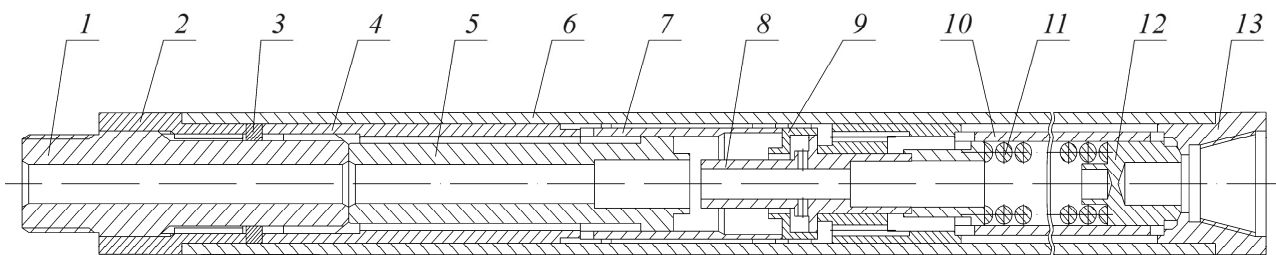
Конструкция погружного гидроударника со встроенным аккумулятором: 1 — наковальня; 2 — гайка ведущая; 3 — полукольца стопорные; 4 — втулка центрирующая; 5 — ударник; 6 — корпус; 7 — гильза ударника; 8 — шток разрядный; 9 — клапан питающе-разрядный; 10 — гильза аккумулятора; 11 — пружина аккумулятора; 12 — поршень аккумулятора; 13 — переходник
